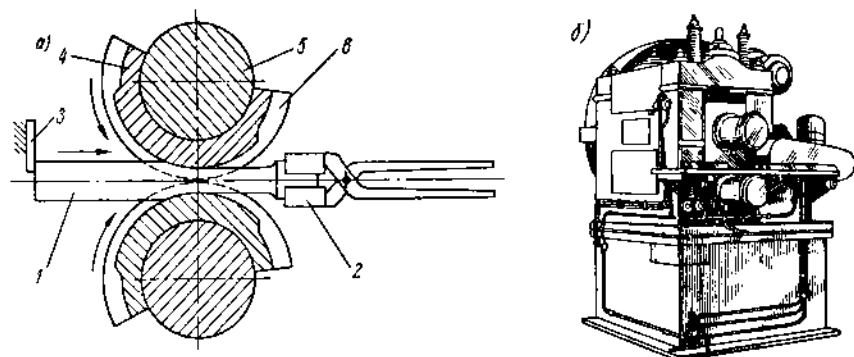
Вальцовка поковок (а), ковочные вальцы (б)
